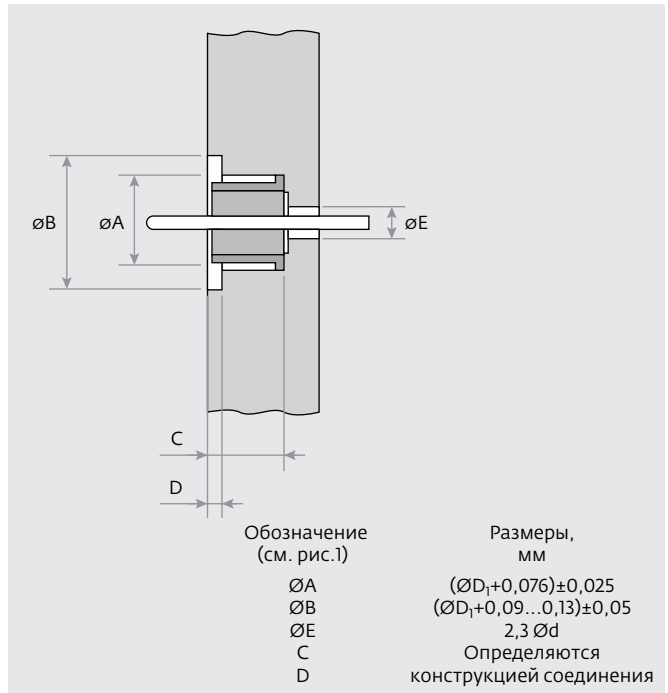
Размеры посадочного места в корпусе изделия под установку СВЧ-вводов
